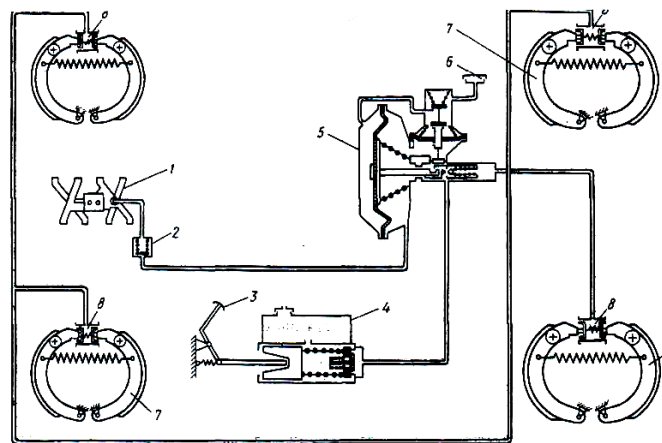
Схема гальмової системи з гідравлічним приводом: 1 – впускний трубопровід двигуна; 2 – запірний клапан; 3 – педаль; 4 – головний гальмовий циліндр; 5 – гідро вакуумний підсилювач; 6 – фільтр; 7 – гальмова колодка; 8 – колісний гальмовий циліндр.
